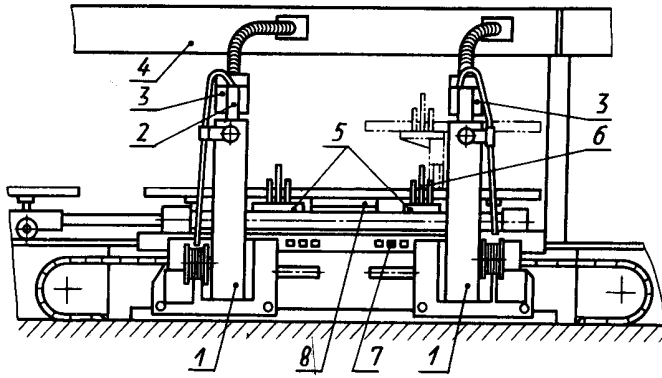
Рабочее место дуговой точечной сварки поперечных балок
